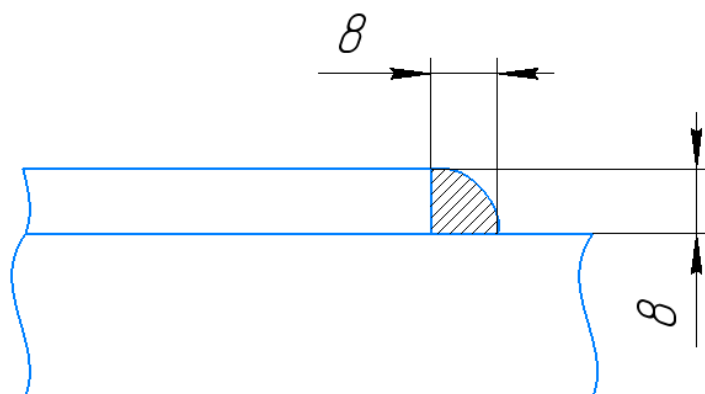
Расчет площадь поперечного сечения наплавленного металла нахлесточного сварного шва
